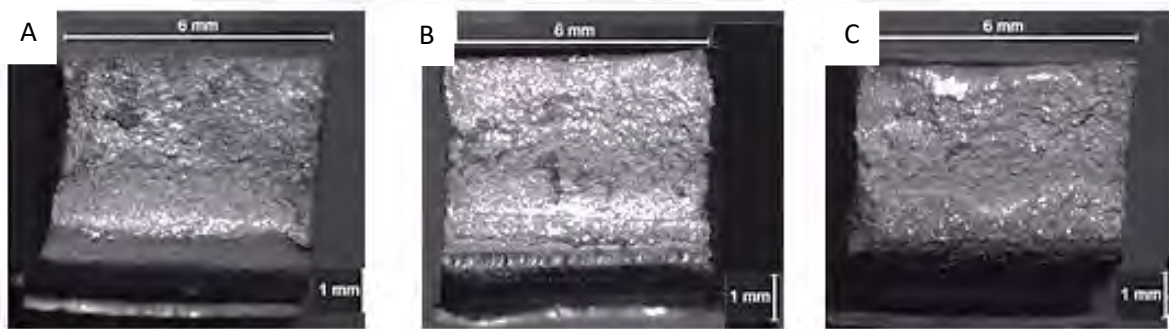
Zonas de fractura de piezas soldadas con pin cónico roscado, 6x6 R1 Etapa 1. A: CR-1700/40 B: CR-1850/40 C: CR-2000/40.
